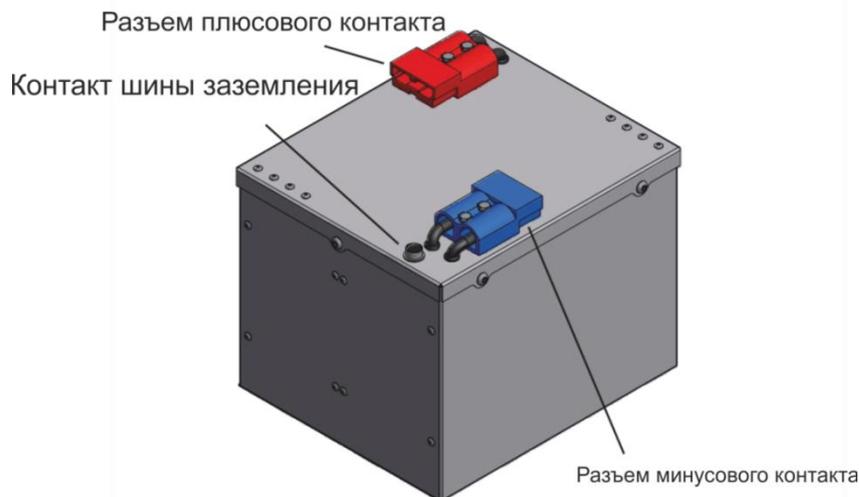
Металлический корпус аккумулятора с разъемами [4]
